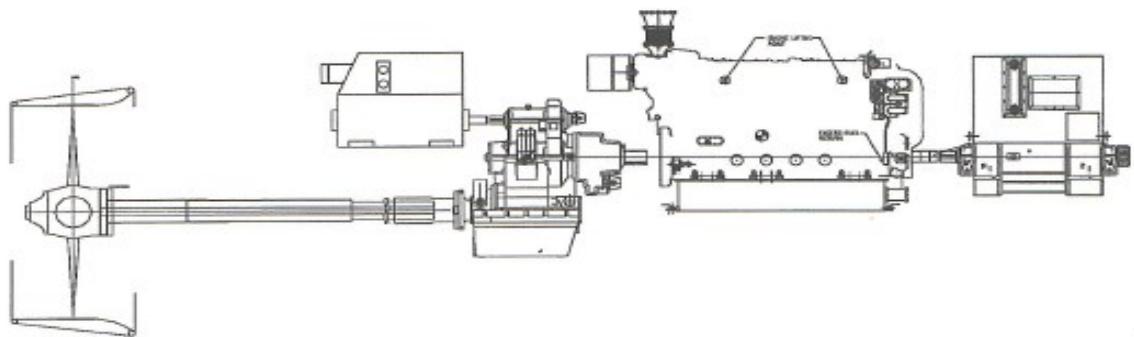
Боковий переріз гребної установки судна BOA DEEP C
